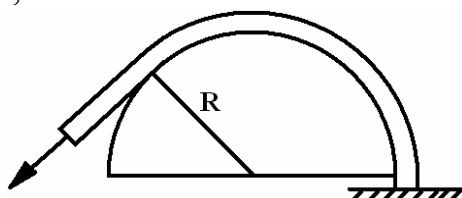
Изгиб образца вдоль цилиндрической поверхности.
